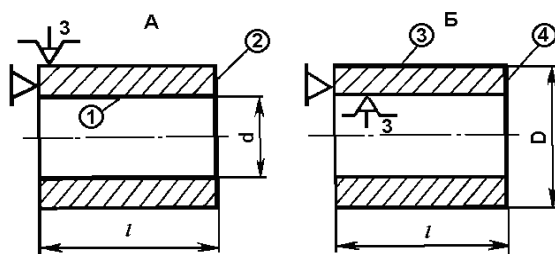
Схема токарной обработки втулки на двух установках.
